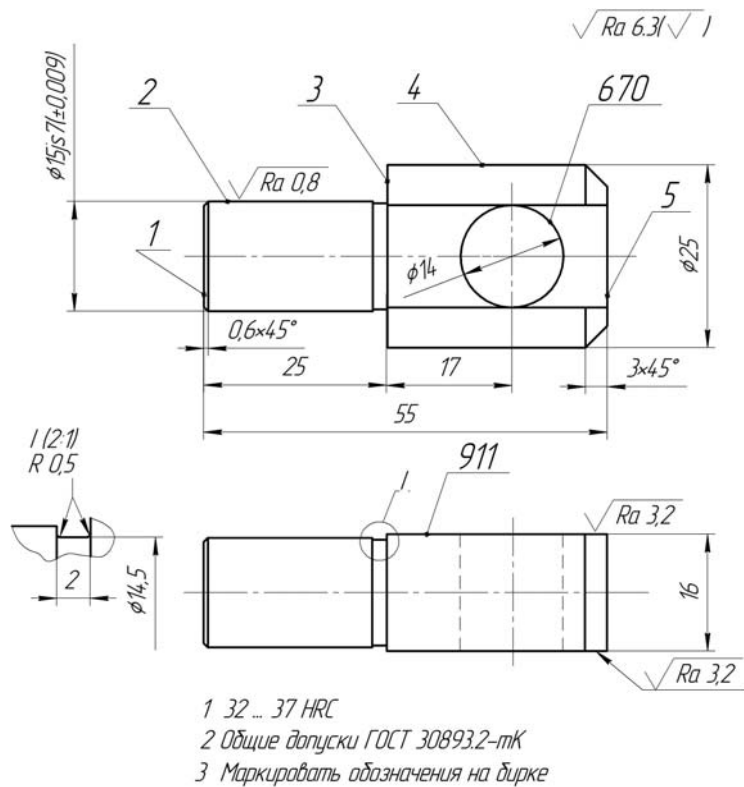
Чертеж детали с цифровым обозначением основных и дополнительных поверхностей
